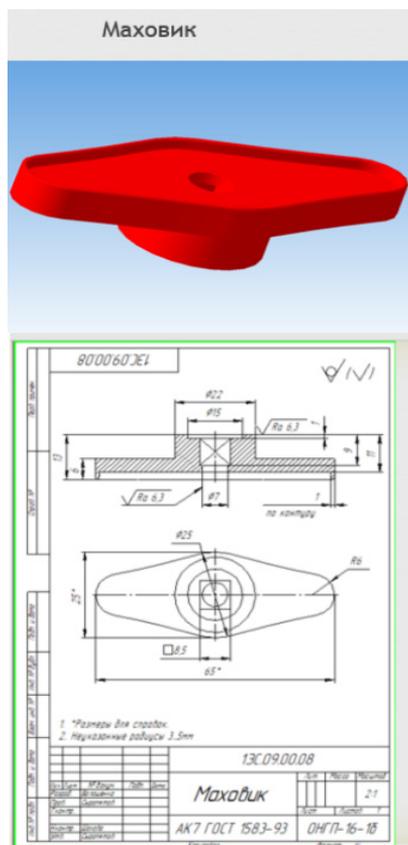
3D-модель и ассоциативный чертеж детали «Маховик», входящей в сборочную единицу
